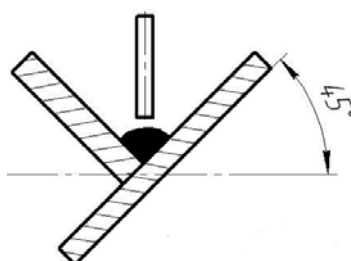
Сварка угловых швов положении в «лодочку»
